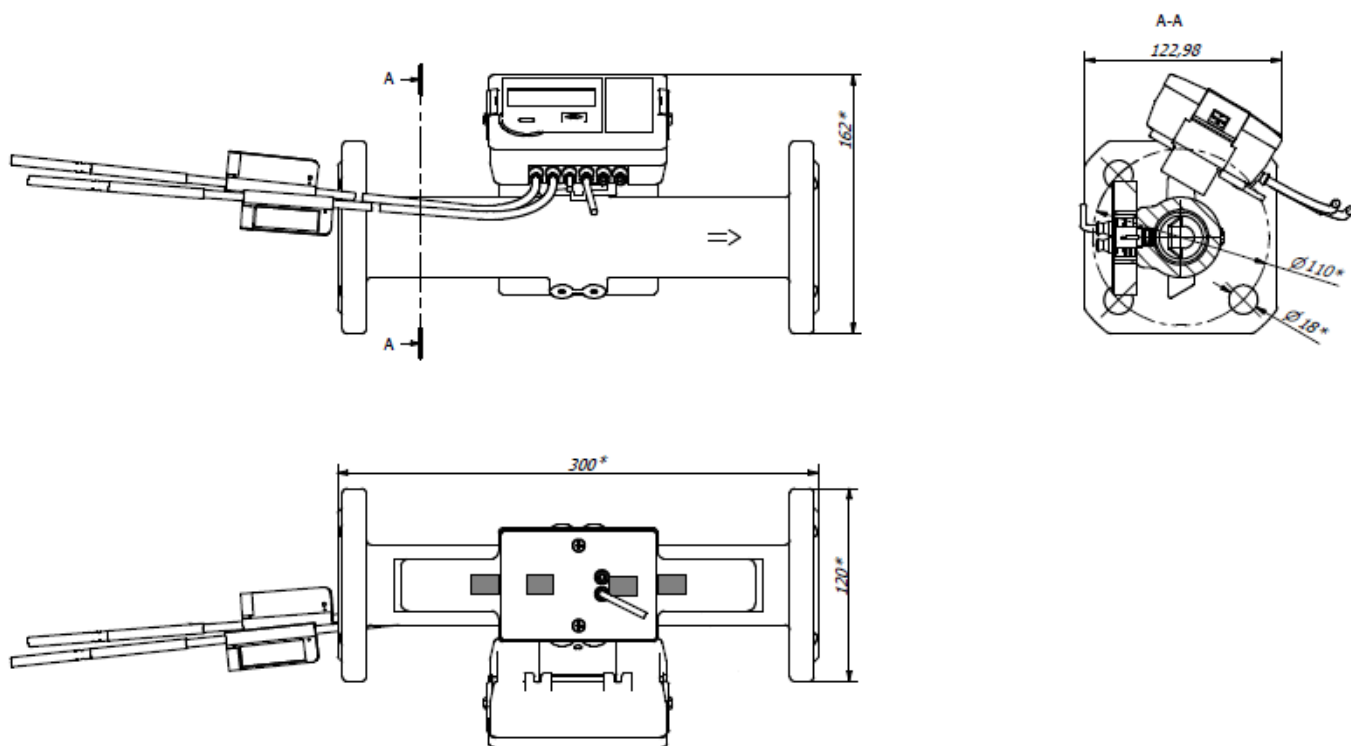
Присоединительный размер к трубопроводу Ду40, длина L =300 мм.
